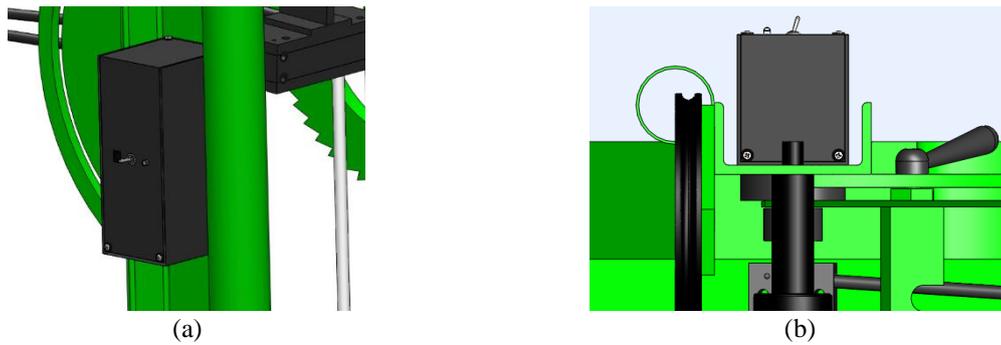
Modelo 3D del montaje del gabinete sobre la máquina Charpy.
